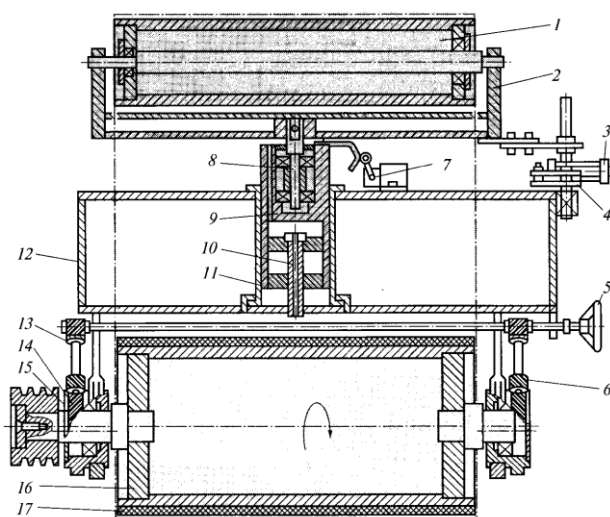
Шліфувальний агрегат з контактним вальцем: 1 – натяжний ролик; 2 – основа; 3 – пневмоциліндр; 4 – механізм осциляції; 5 – маховичок; 6 – зубчасте колесо; 7 – вимикач; 8 – вісь; 9 – гільза; 10 – шток; 11 – склянка; 12 – траверса; 13 – черв'ячна передача; 14 – сектор; 15 – втулка; 16 – валець; 17 – гумове покриття
